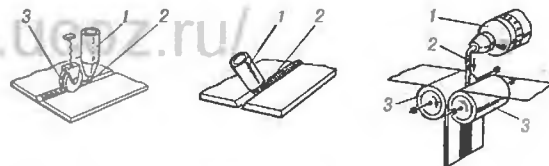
Схема зварювання термопластів екструдованою присадкою:
